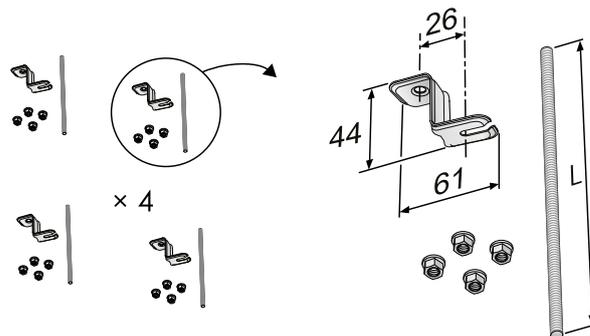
Accessoire d'installation SYST MS M8-1, montage au plafond et sur tige filetée
